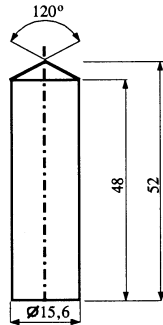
Цилиндрический бронзовый поршень; размеры в мм
